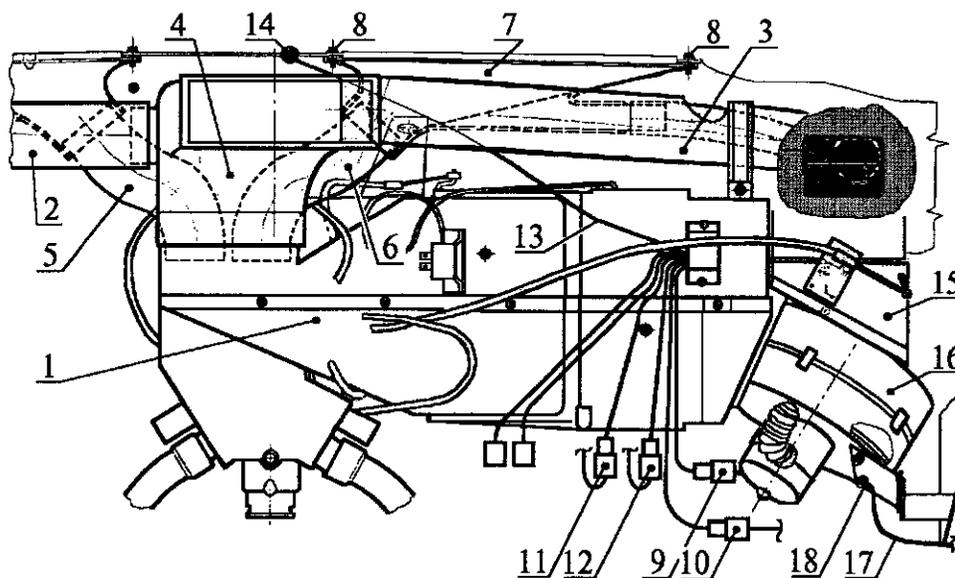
Установка соединителя короба воздухозаборника и вентилятора, подсоединение проводов и воздуховодов к блоку обработки воздуха:
